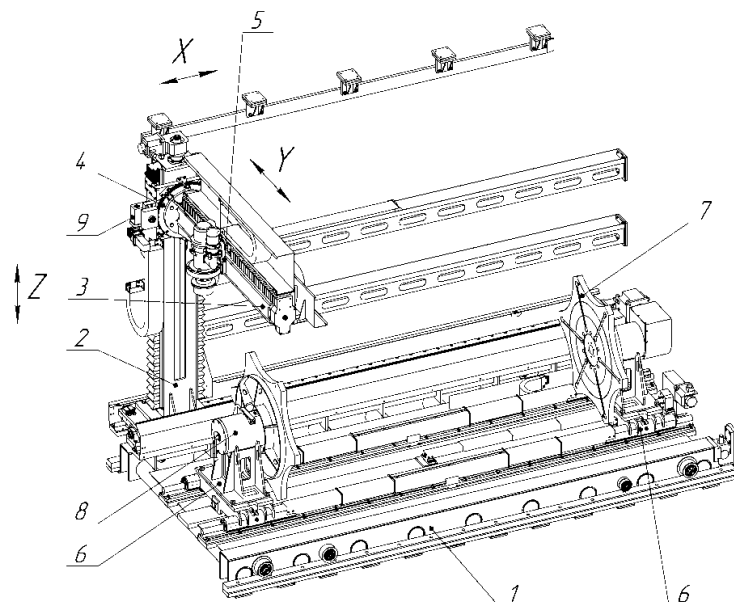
Станочный комплекс (1 - платформа, 2 - колонна, 3 - траверса, 4 - механизм поворота траверсы, 5 - механизм поворота пушки, 6 - каретка, манипулятор изделия, 8 - задняя бабка 9 - редуктор)
